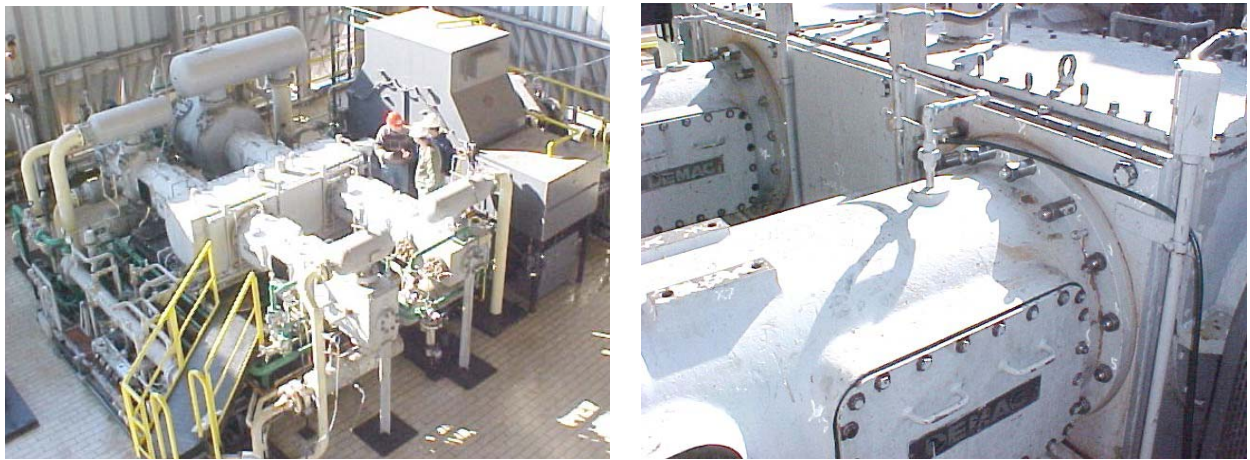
Pré-compressor de cinco estágios identificando o modo de fixação do flange à carcaça através de parafusos prisioneiros.
